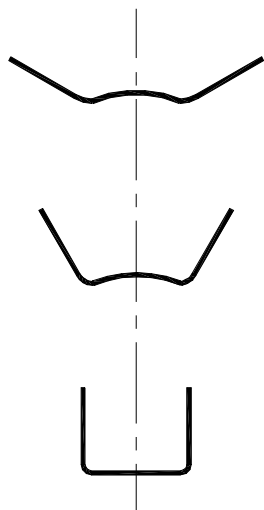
Изготовление профиля с промежуточным формованием выпуклого дна
